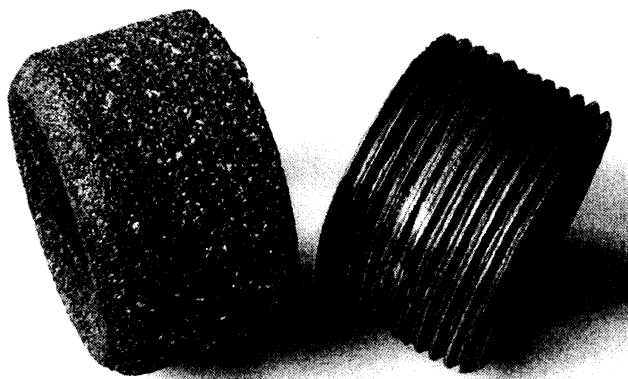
Внешний вид отливки и готового изделия «Ниппель 1/4»
